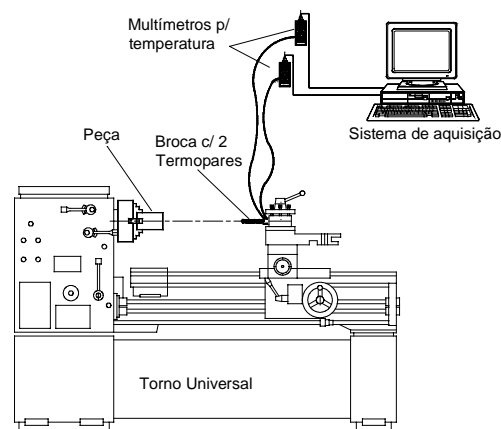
Desenho esquemático da montagem experimental - sistema de aquisição.
